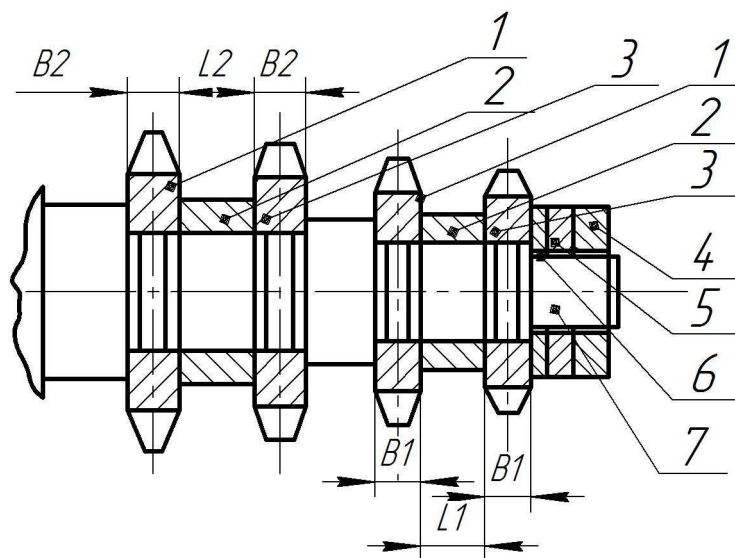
Вид сборного инструмента, собранного из дисковых фрез
